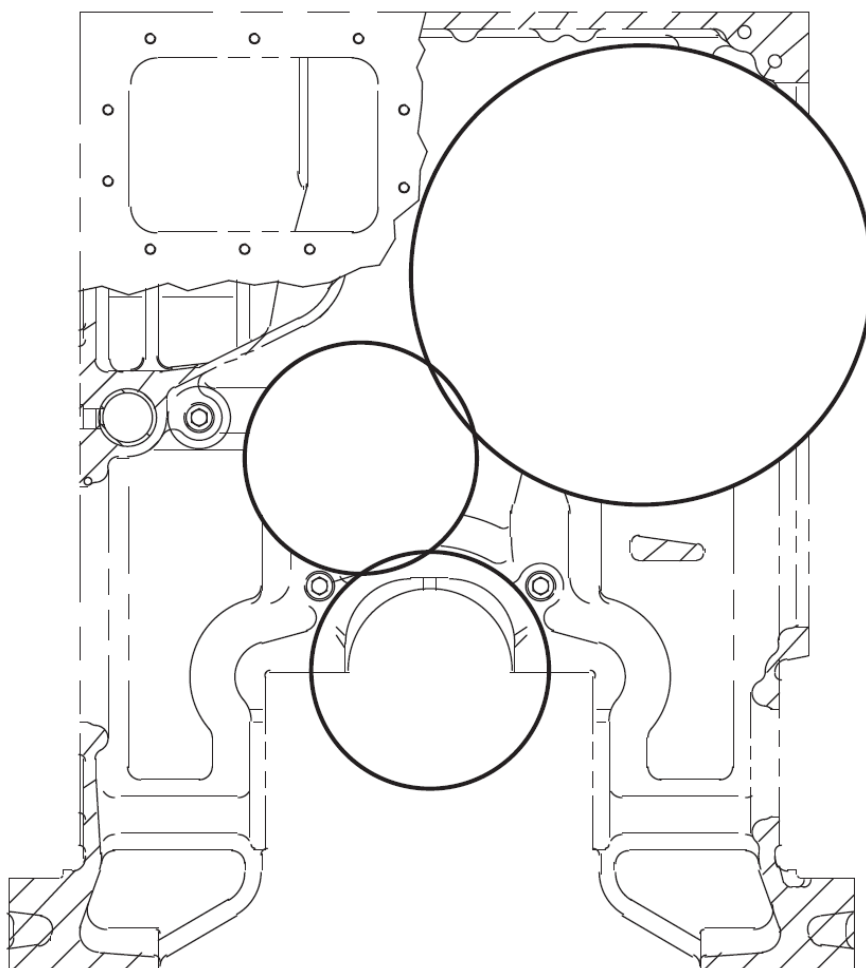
Схема розташування шестерень приводу розподільного вала
